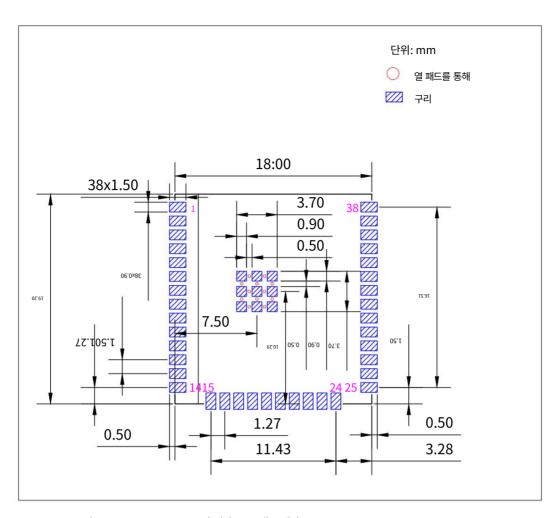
ESP32WROOM32U의 권장 PCB 랜드 패턴
